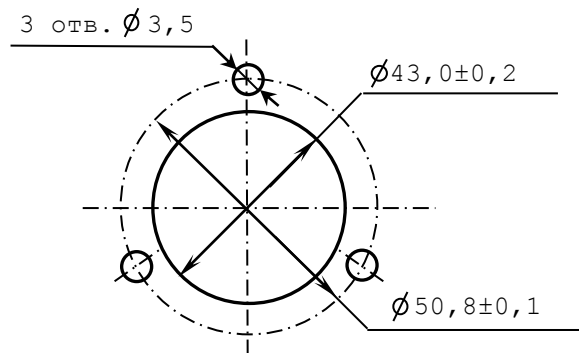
Установочные размеры штурвала WSB
